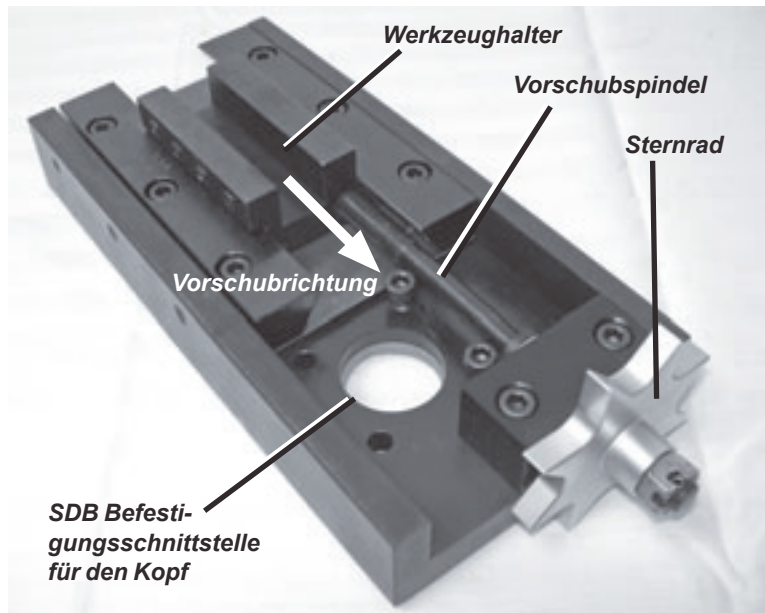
Der Flanschflächenschlitten wird an der SDB 103 montiert, um Flansche planzusenken.
